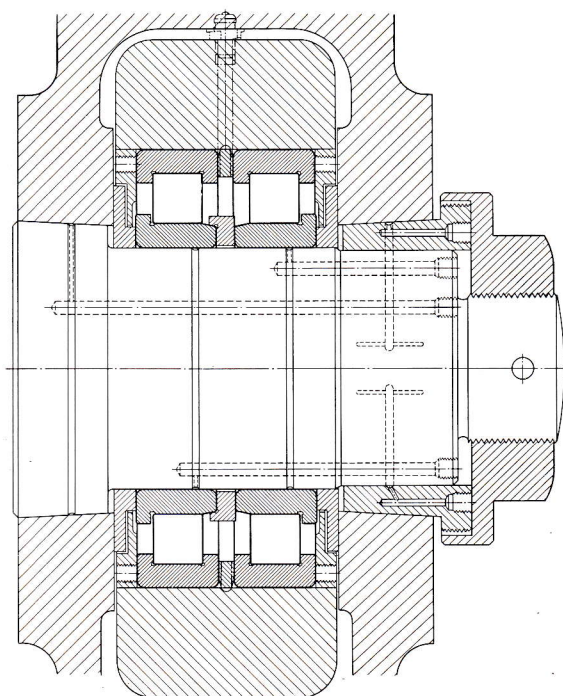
Disposición de rodamientos para la cruceta en locomotoras a vapor
